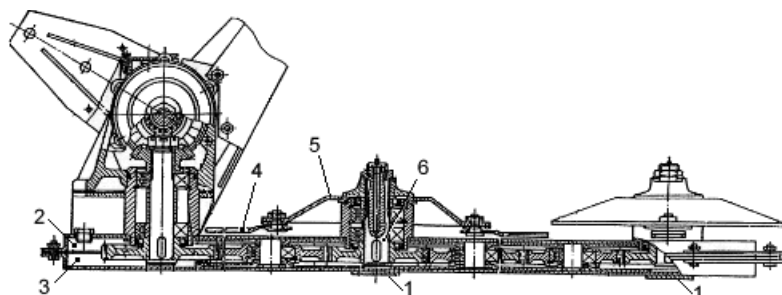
Конструкция многороторного рабочего органа косилки с боковым приводом
